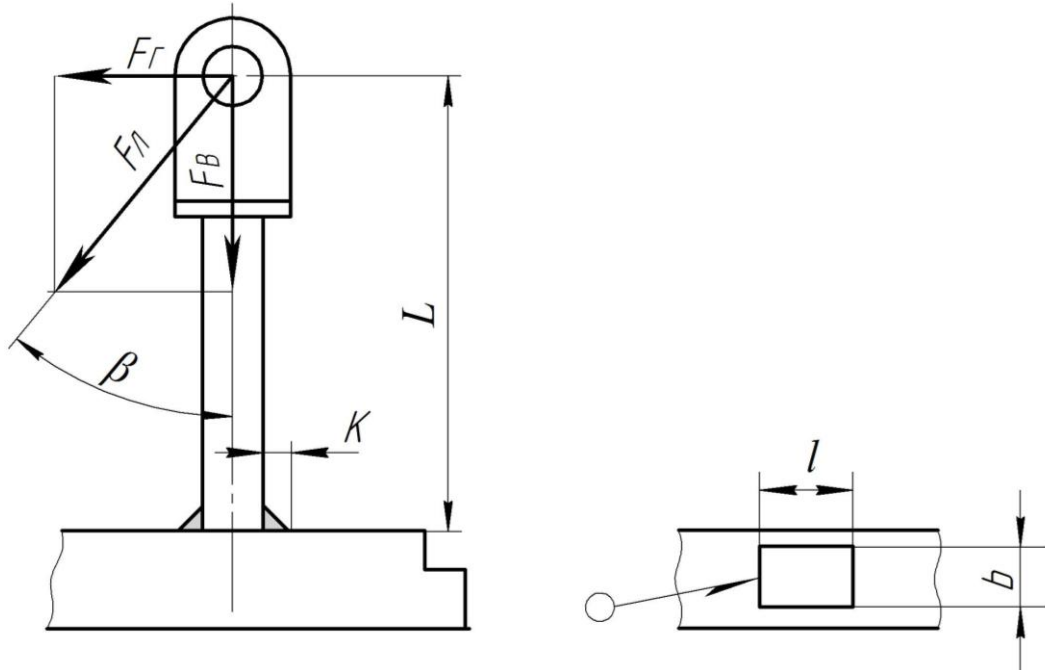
Схема навантаження зварного з'єднання стійки
